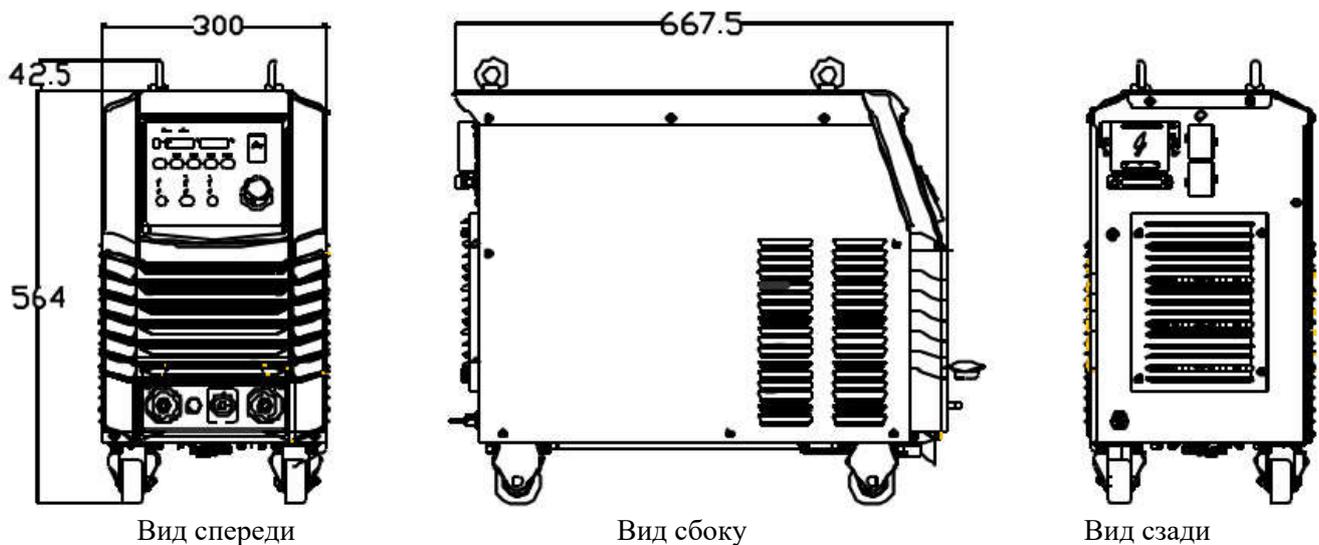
Габаритные размеры сварочного аппарата (мм)
